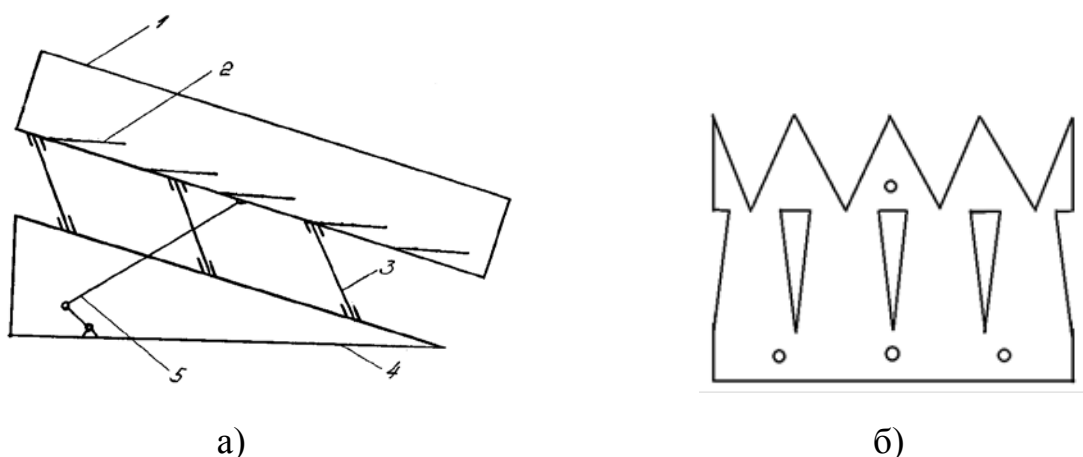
Лабораторно-экспериментальный вибрационный смеситель сыпучих кормов. а) общий вид: 1 – виброжелоб; 2 – перемешивающий элемент; 3 – рессора; 4 – рама; 5 – шатун. б) плоский перемешивающий элемент с треугольными отверстиями.
